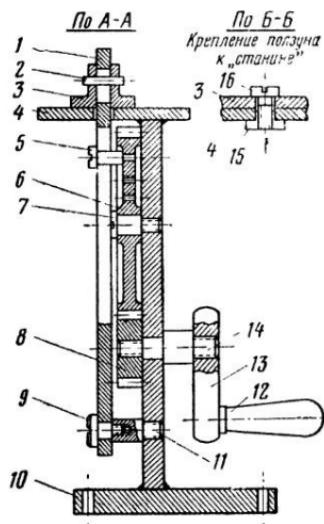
Модель привода поперечно-строгального станка (схема соединения деталей): 1 — кулиса; 2 — шпилька; 3 — «ползун»; 4 — «станина»; 5 — «камень» кулисы; 6 — ведомое зубчатое колесо («маховое»); 7 — ось; 8 — ведущее зубчатое колесо; 9 — винт крепления кулисы; 10 — основание; 11 — ось кулисы; 12 — ручка; 13 — рычаг ручки; 14 — вал привода; 15 — сухарь; 16 — винт.
